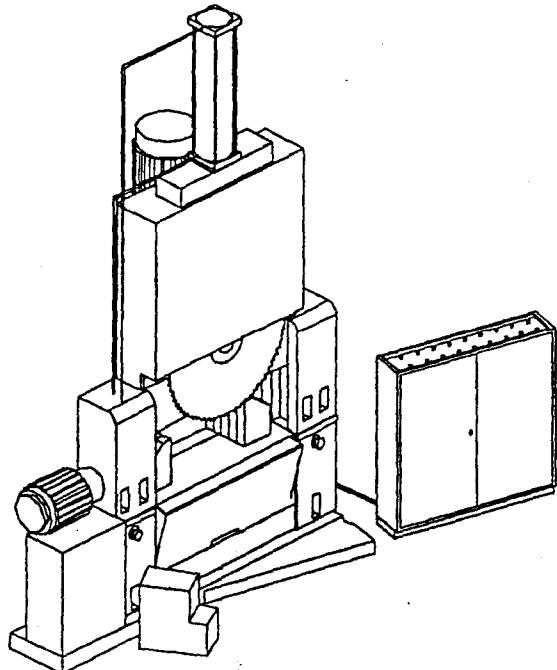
а — Вертикальний круглопильний верстат з двома стояками
